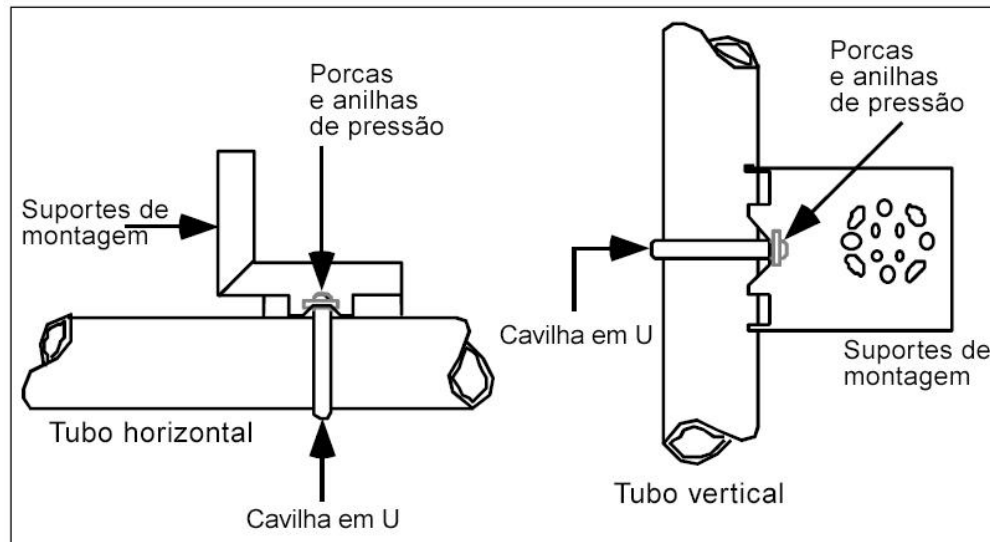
Suporte de montagem em ângulo fixo a um tubo horizontal ou vertical
